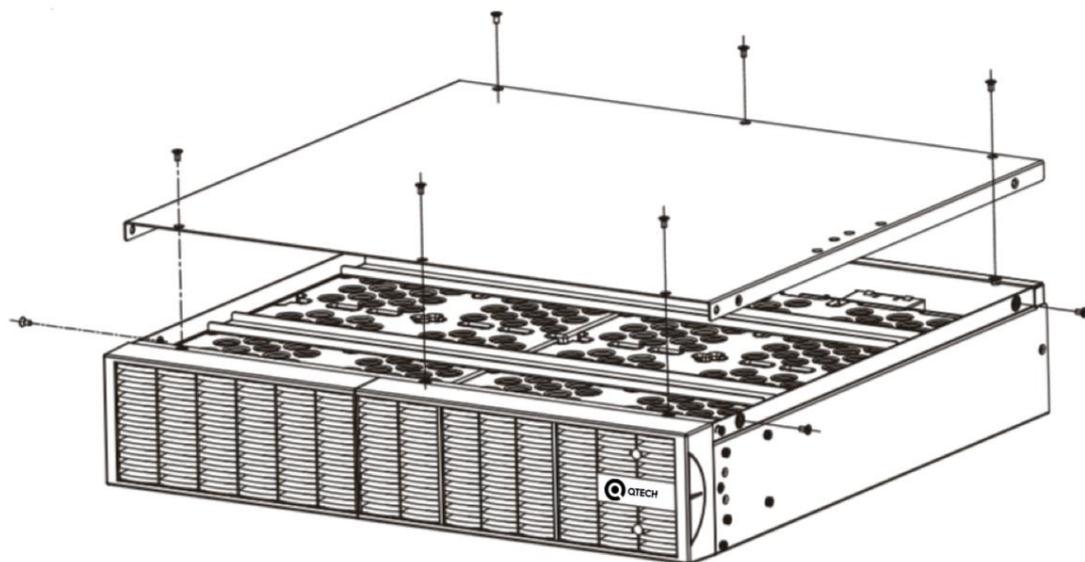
Установка верхней крышки Батарейного модуля
